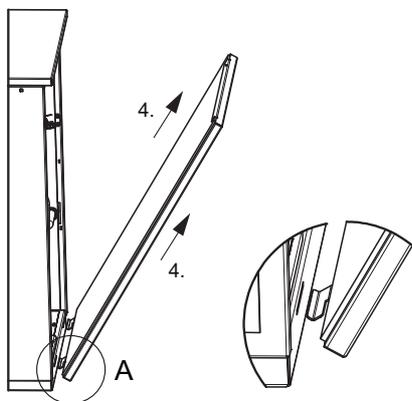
Apertura delle lamiere di copertura laterali, passaggio 4
